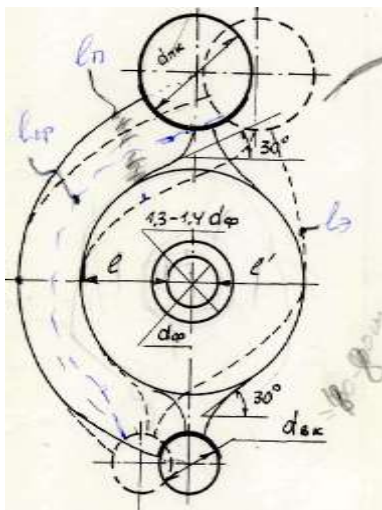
Схема размещения почной камеры, коллекторов и поверхностей нагрева
